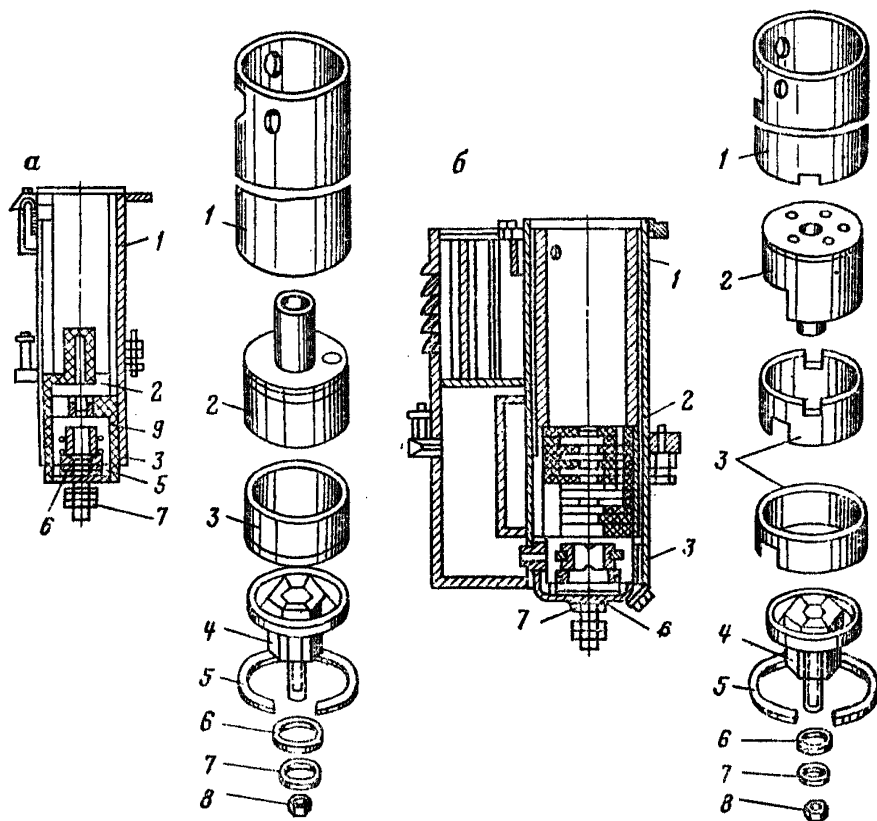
Разрез цилиндра выключателя типа ВМГ-133 и последовательность разборки его деталей:
